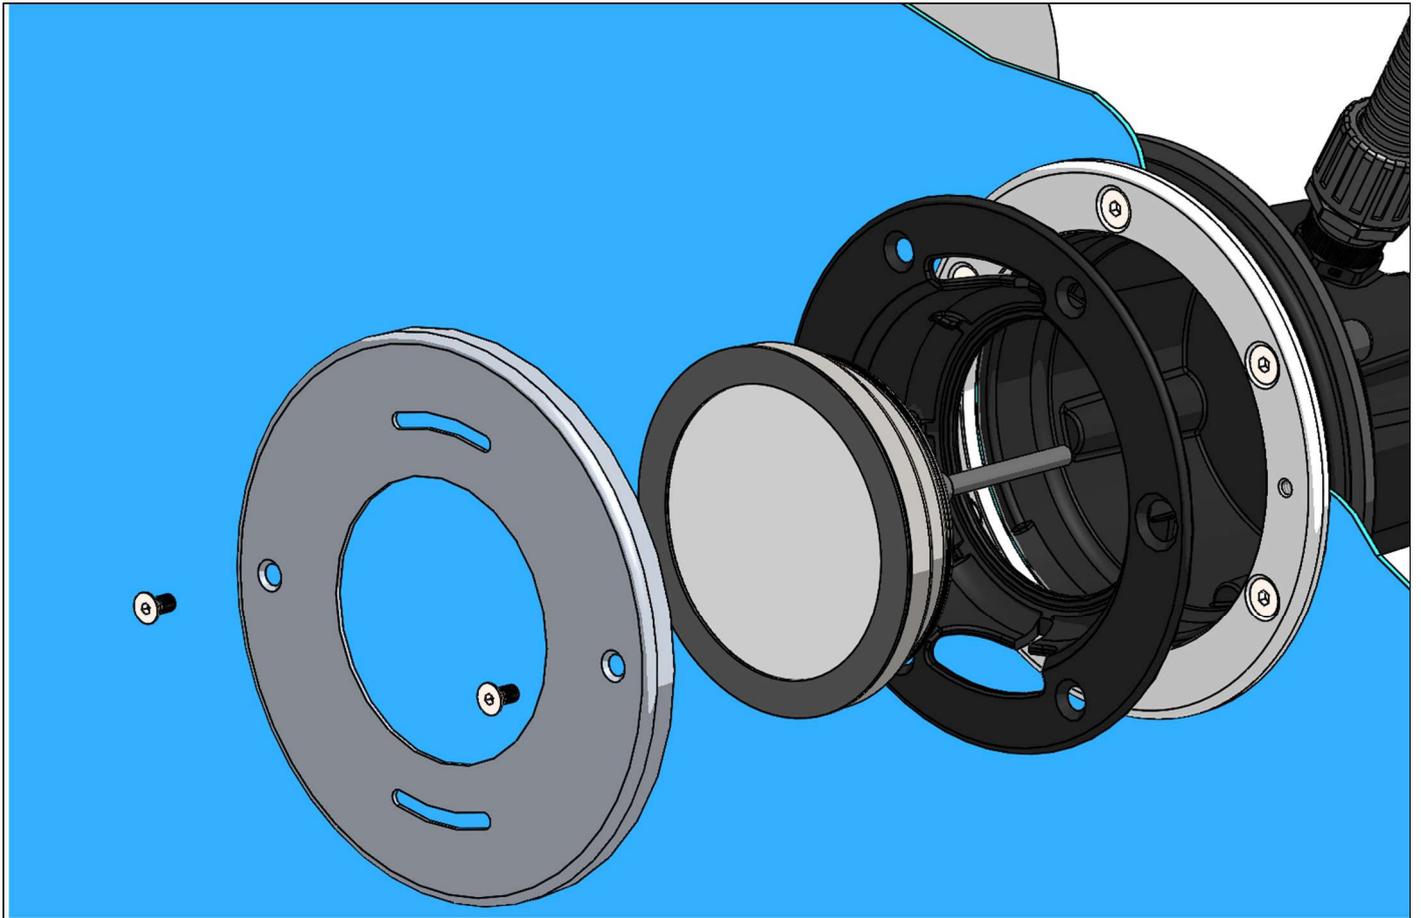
Kit di montaggio della piscina in cemento con pellicola sigillante
